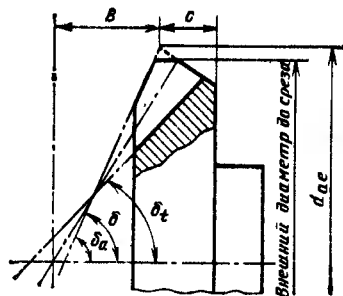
Основные размеры заготовки под круговое протягивание
